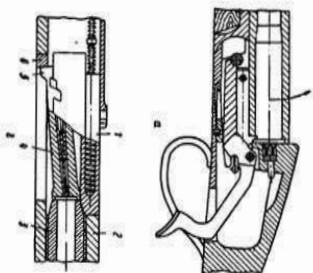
Конструктивные схемы неперемещающегося (а) и перемещающегося (б) затвора: 1 — затворная рама; 2 — ствольная коробка; затвор: 3 — боевой упор затвора; 6 — скелетный упор ствольной коробки
